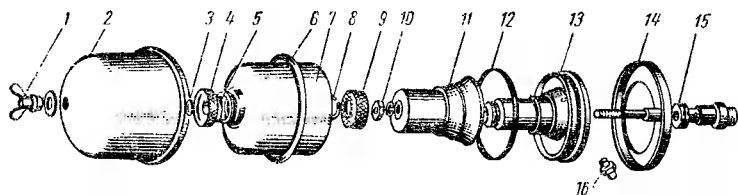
Фильтр центробежной очистки масла двигателя ЗМЗ-53:
